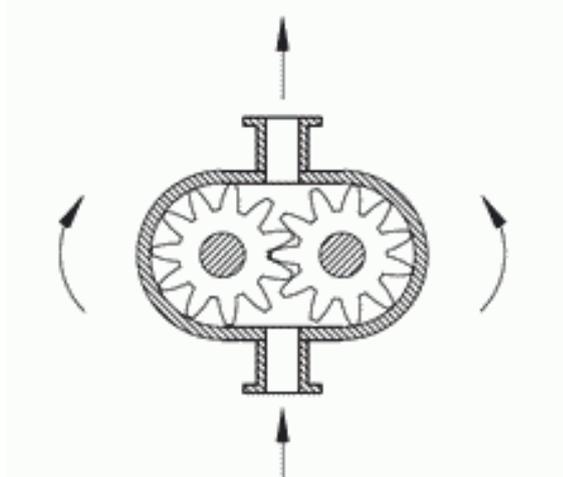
Шестерёнчатый насос с внешним зацеплением.
